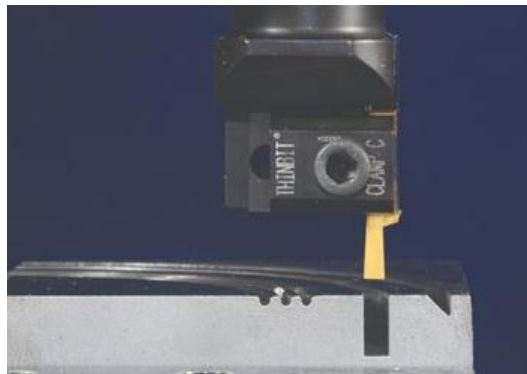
Спеціальний інструмент для нарізання канавок компанії Thinbit/Kaiser Tool Co. [12]
